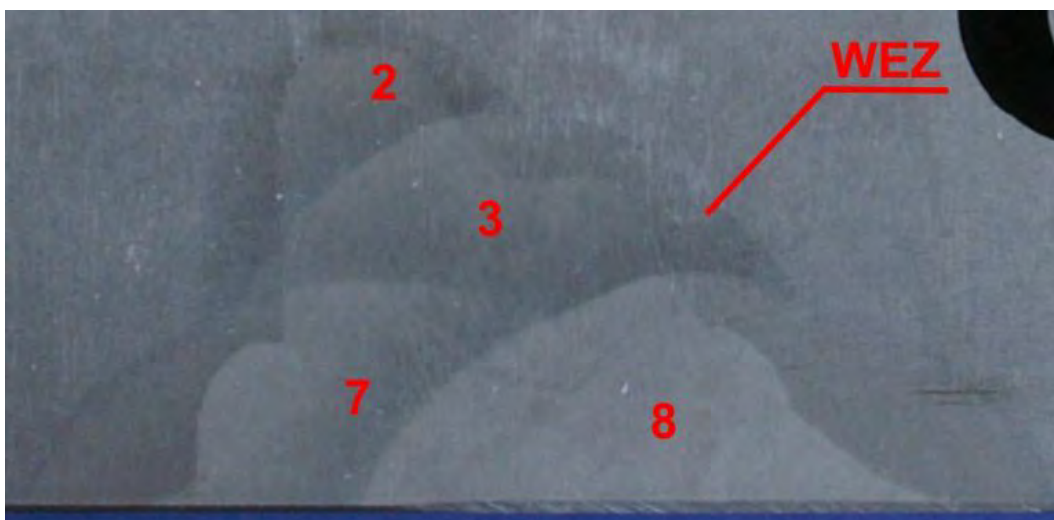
Probe 03 - Ansicht unterer Teil der Schweißnaht
